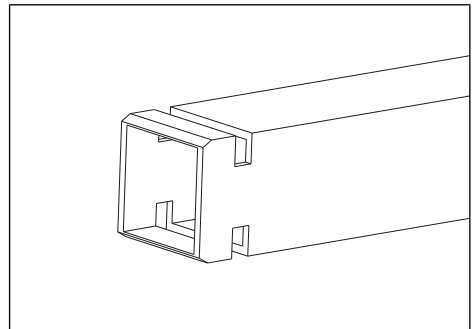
Évidements dans la poutre transversale Multi Wall
